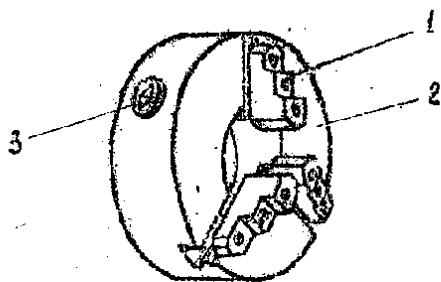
Трёхкулачковый самоцентрирующий патрон.
